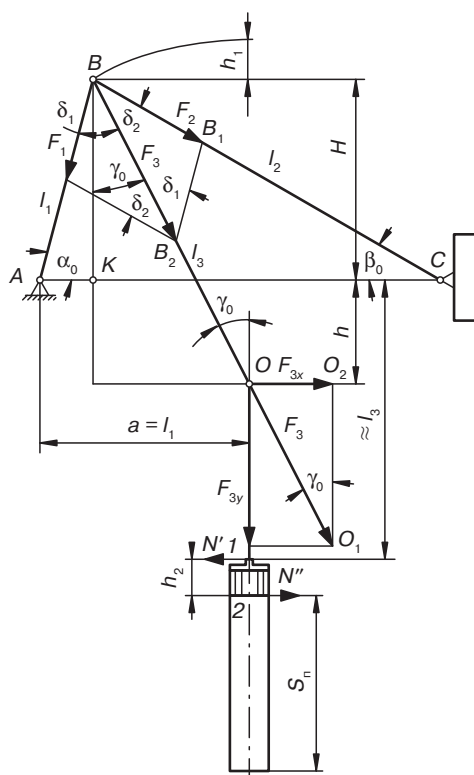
Схема шестизвенного механизма с неподвижным гидроцилиндром
